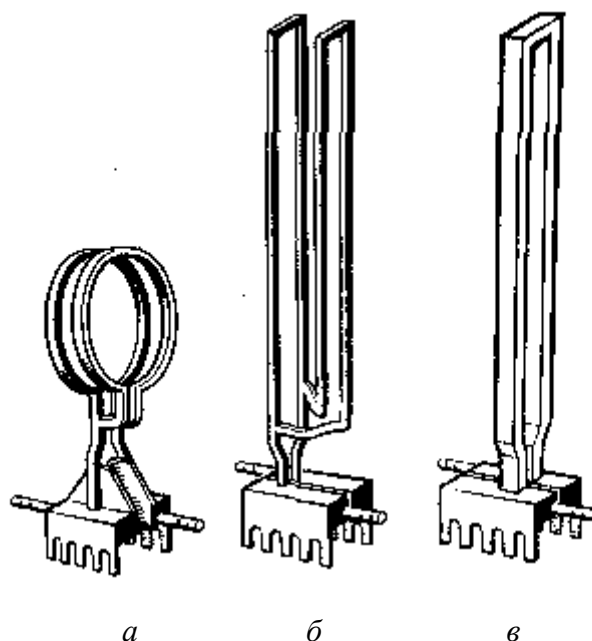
Индукторы для нагрева наружных наплавляемых поверхностей:
